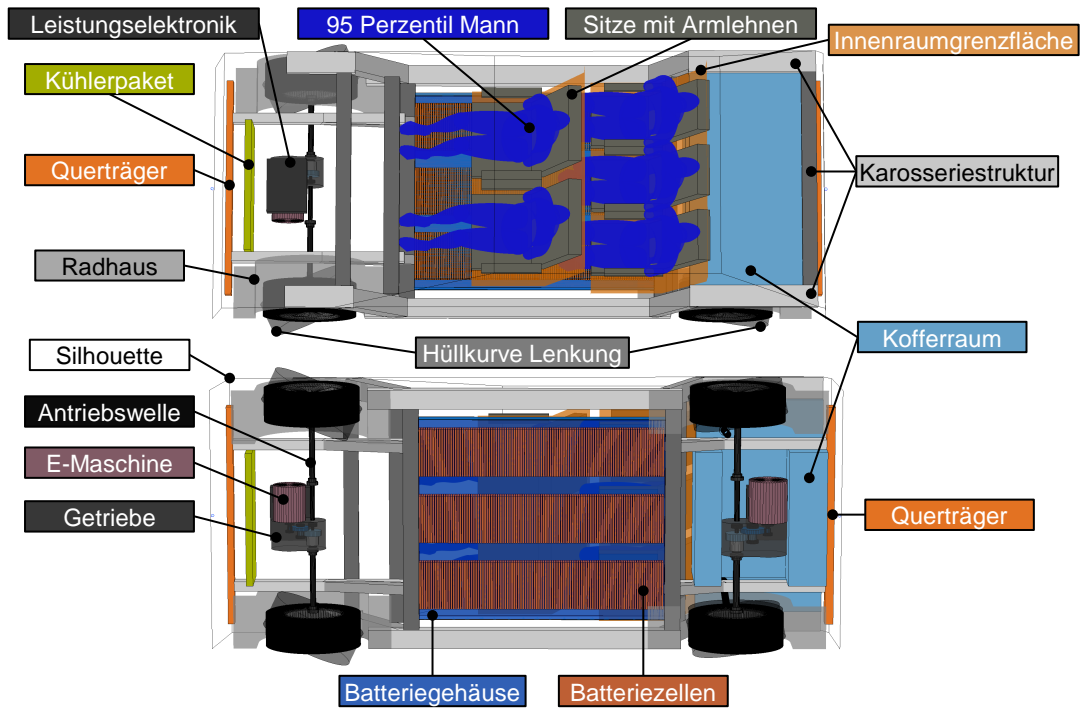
Komponenten im Fahrzeugpackage des AuVeCoDe-Tools [145]
